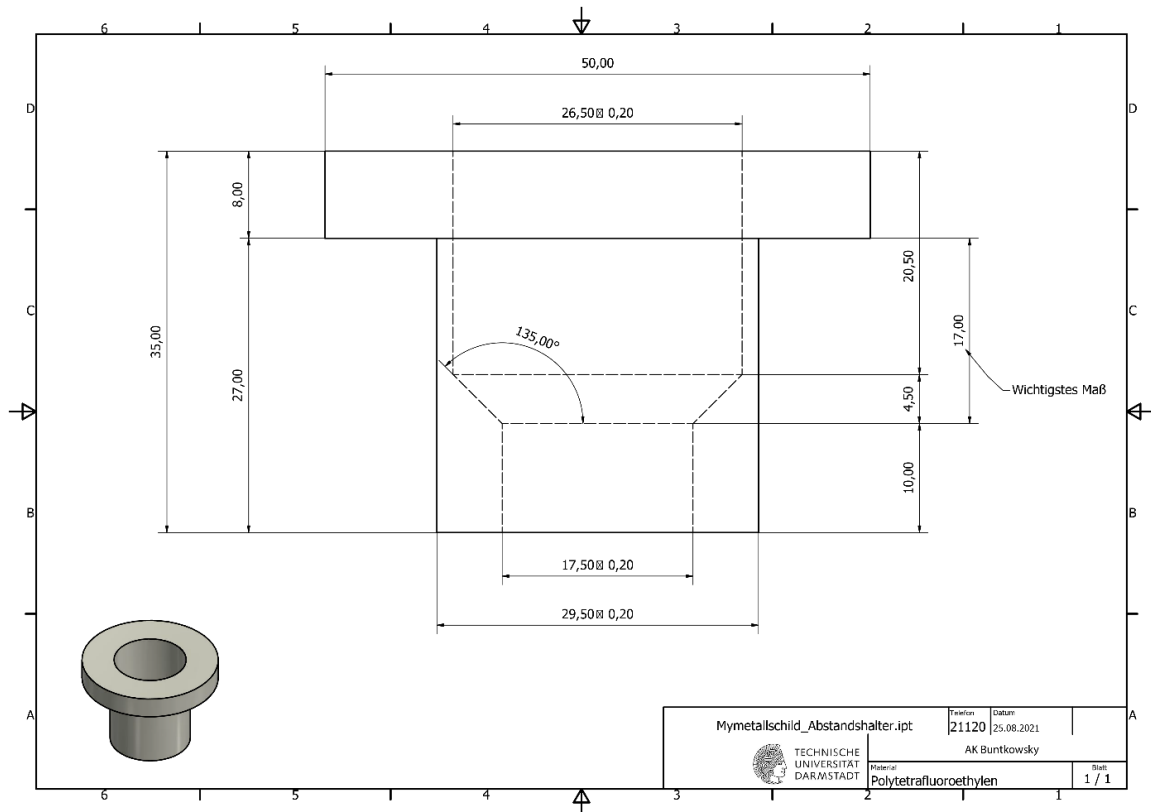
Technische Zeichnung des Inserts für das  $\mu$ Metallschild, um die Proben zu positionieren.
